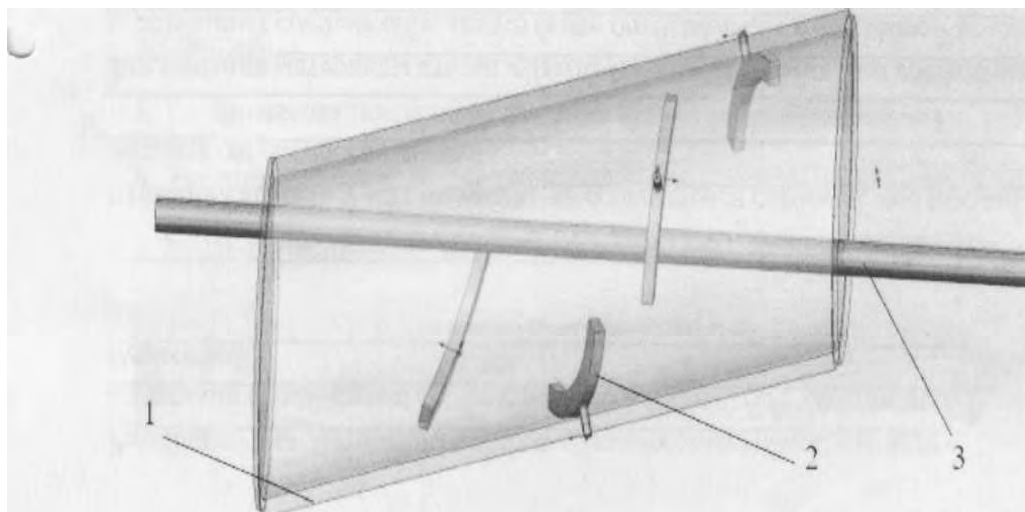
Разработанная конструкция барабанного смесителя: 1 – корпус; 2 – перфорированная лопасть; 3 – вал
